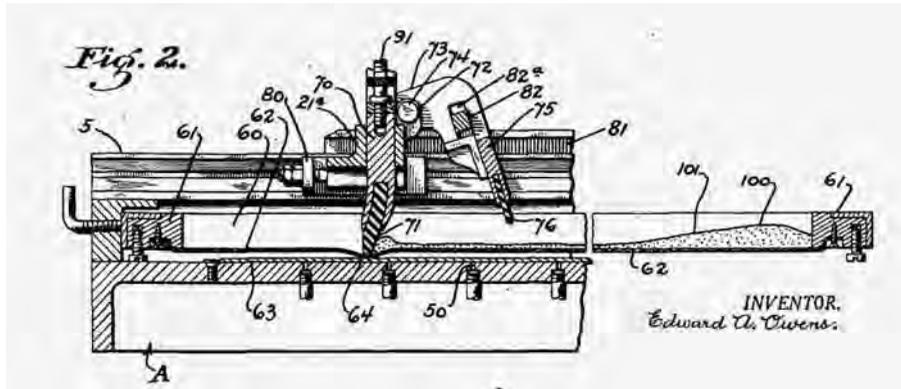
E. A. Owens. *Stencil Printing Machine*. (1933). Máquina con base aspirante y mecanismo de raqueta y contrarraqueta. Anexo 1. Pat. 1.922.710
